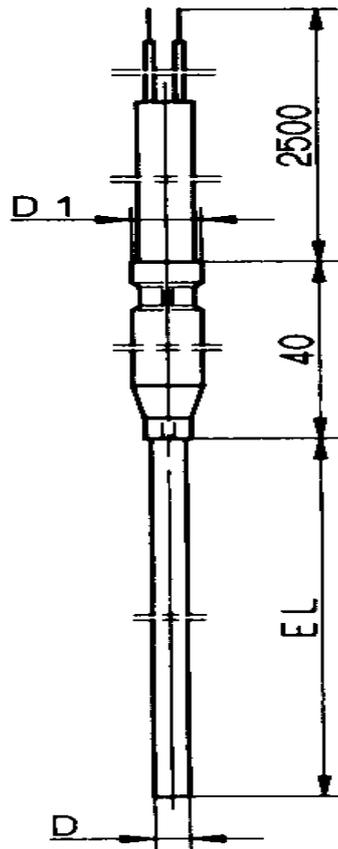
铠装(矿粉隔离)型热偶外形尺寸 2
